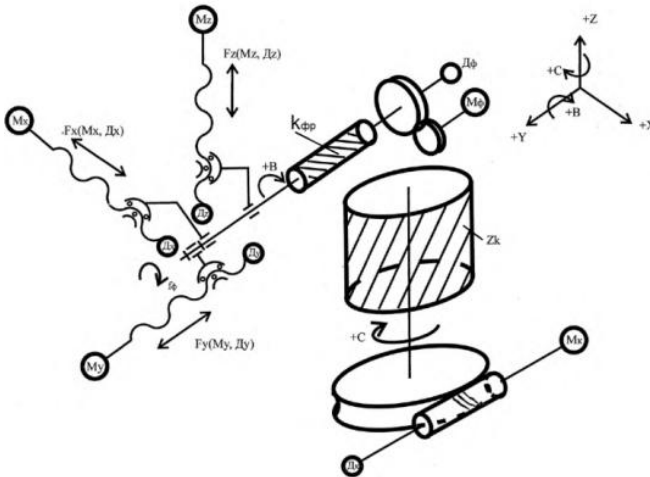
Структурна схема зубофрезерного верстата з ЧПК
